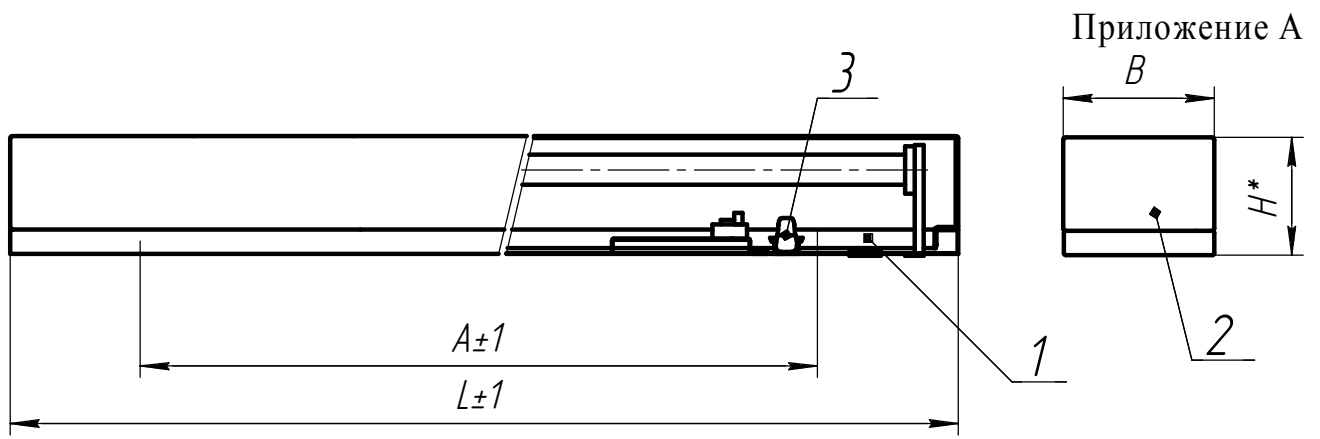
ЛПО46-18; 36; 2x18; 2x36 1. корпус в сборе; 2. рассеиватель; 3. защелка
